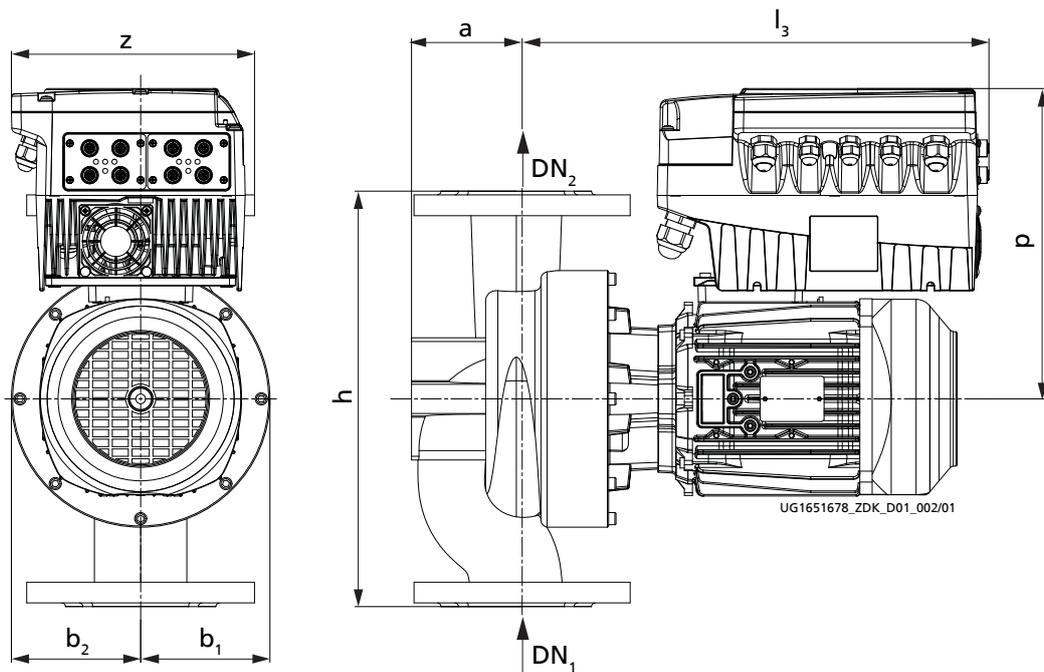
Abmessungen Pumpenaggregat mit PumpDrive 2 Eco, mit Flanschanschluss, Baugröße ≥ 032-032-100
